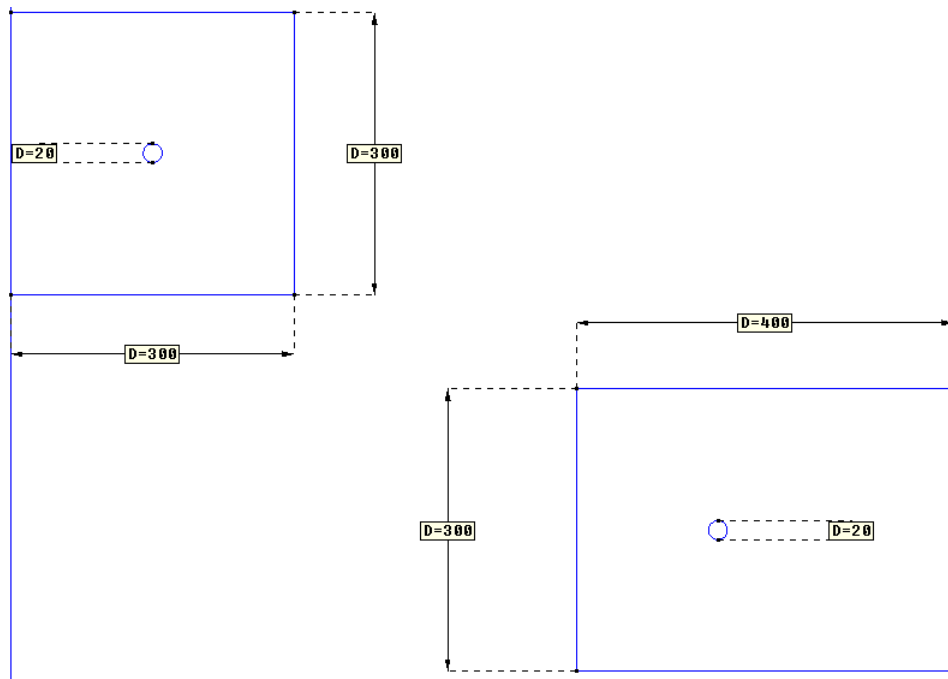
Vista en detalle (pozos) de las cotas en el Plano XY
